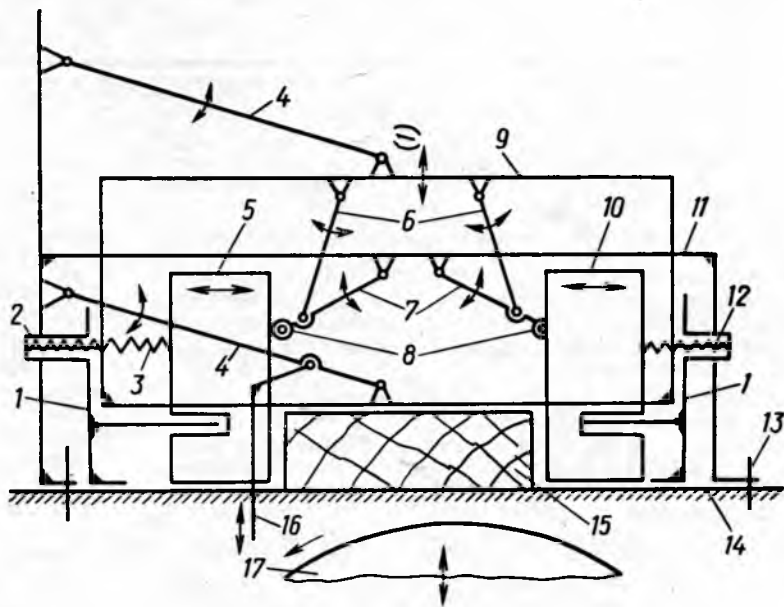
Кинематическая схема звукоизолирующего устройства с боковыми раздвижными стенками:
